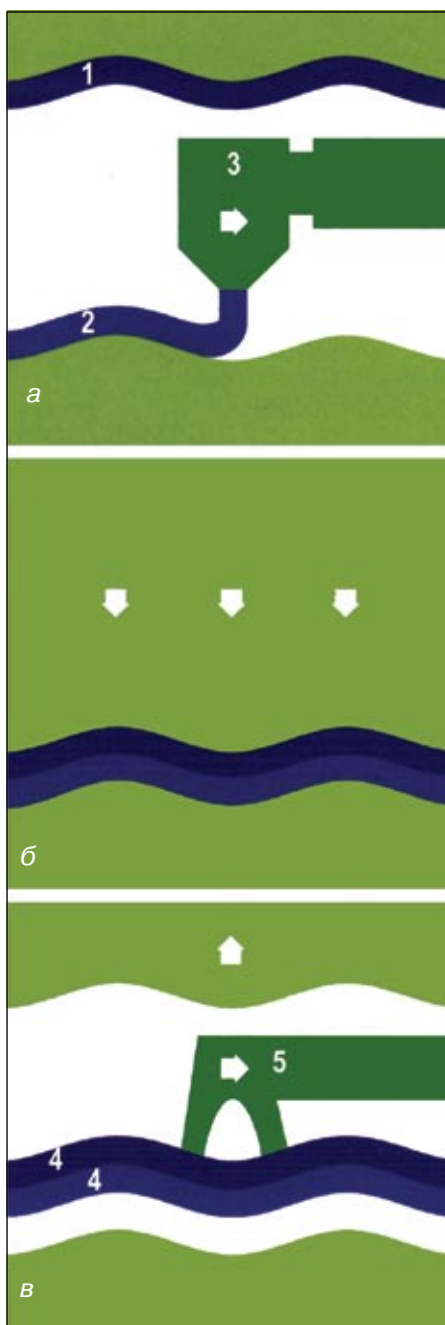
Схема комбинированного экструзионно-прессового процесса Tecomelt изготовления деталей с большой площадью поверхности: а - формирование заготовки детали для прессования (1 - декоративная текстильная заготовка; 2 - слой расплава ПМ; 3 - экструзионная головка); б - прессование комбинированной заготовки детали; в - удаление готовой детали (4 - готовая деталь; 5 - схватывающее устройство) (источник: Engel)
